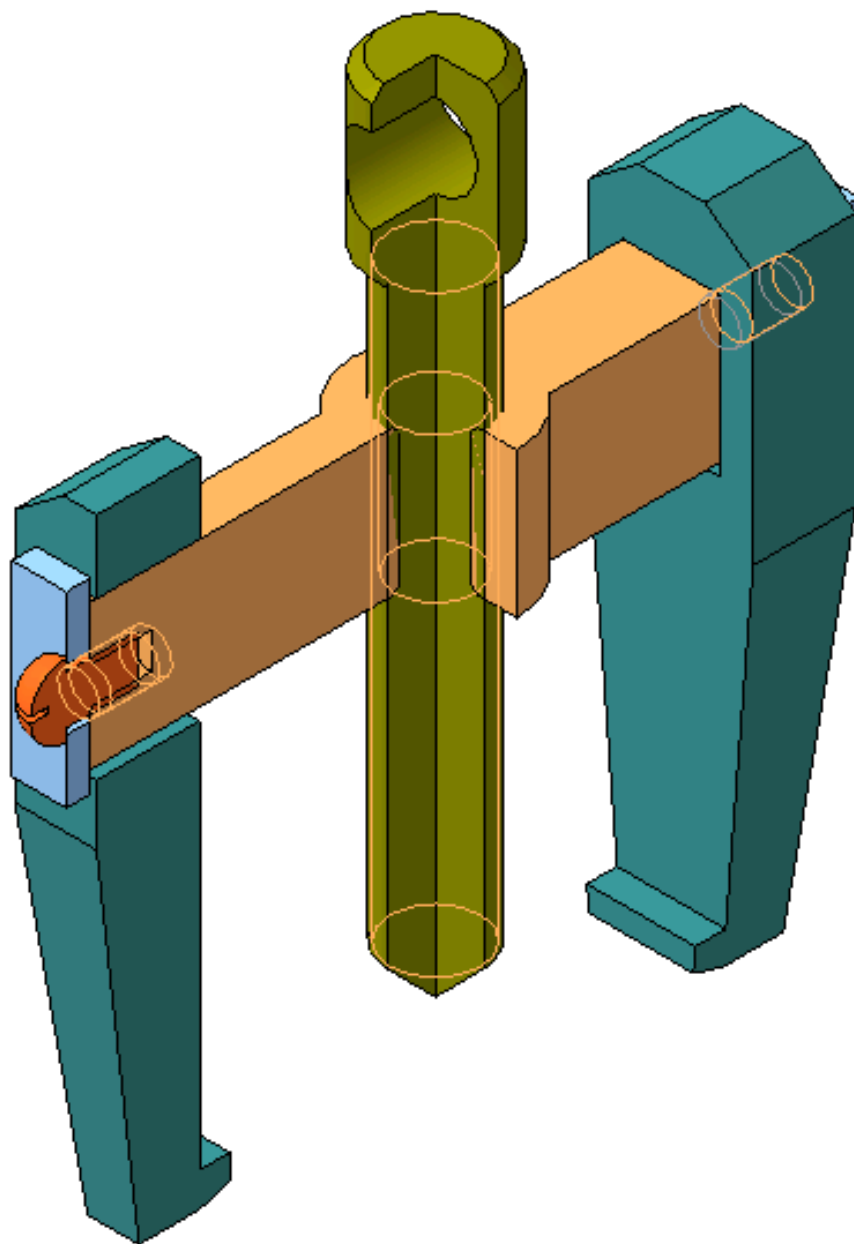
3D-модель сборки изделия «Съемник-1» (варианты 6, 26)
